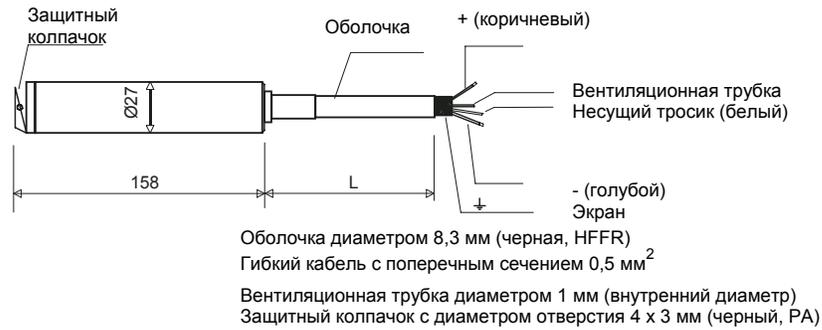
Измерительный преобразователь 7MF1570, размеры
